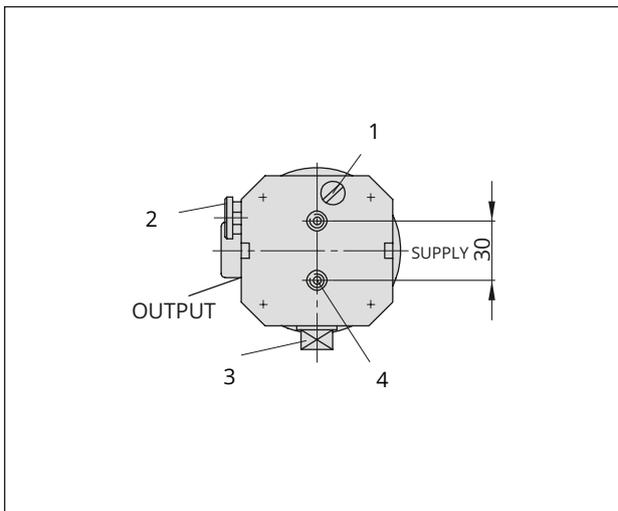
Maße in mm · Rückansicht Typ 6116 ohne Anbauteile
